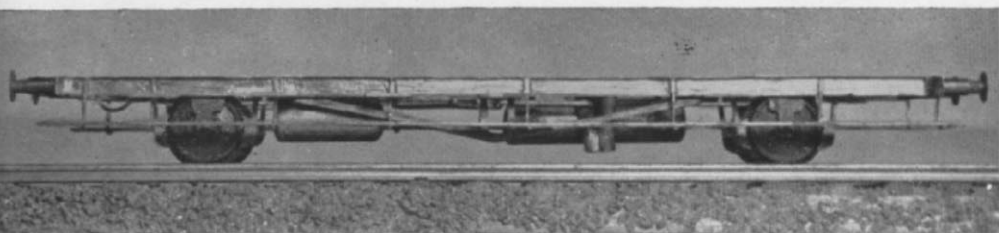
u. 11. Anschließend an Untergestell durchgehende Zughakenstange, Abortabfallrohre, Puffer und Fußtritte anbringen. Ausführung und Anbau der Zugvorrichtung (Kupplung) bleibt dem Erbauer überlassen.
